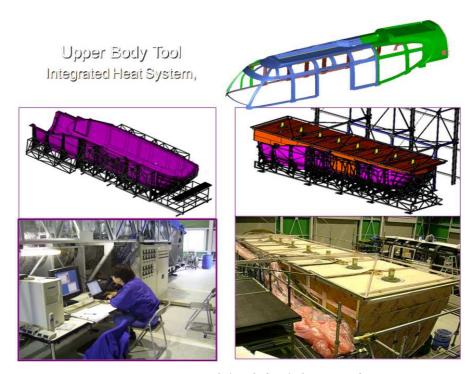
Vacuum Infusion 공법을 위한 대형 Tool 및 Heat system
